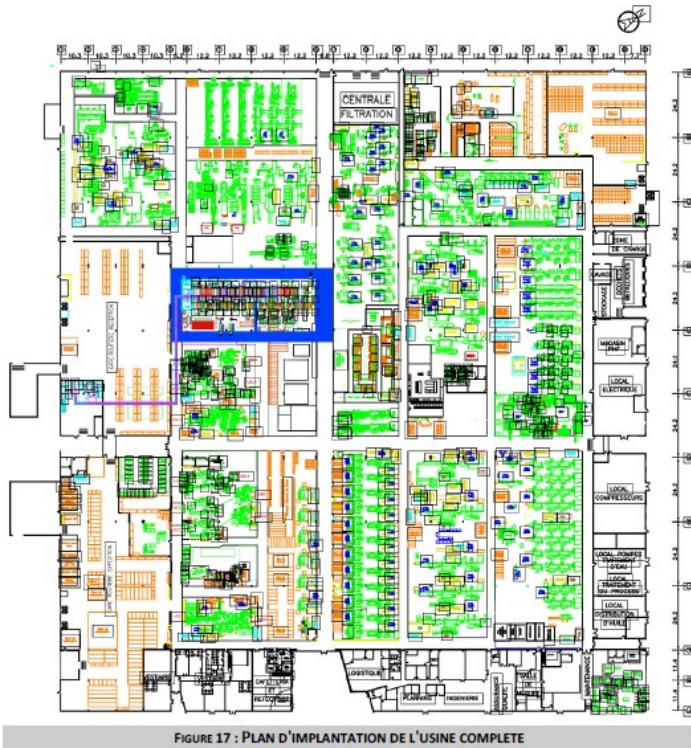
PLAN D'IMPLANTATION DE L'USINE COMPLETE
